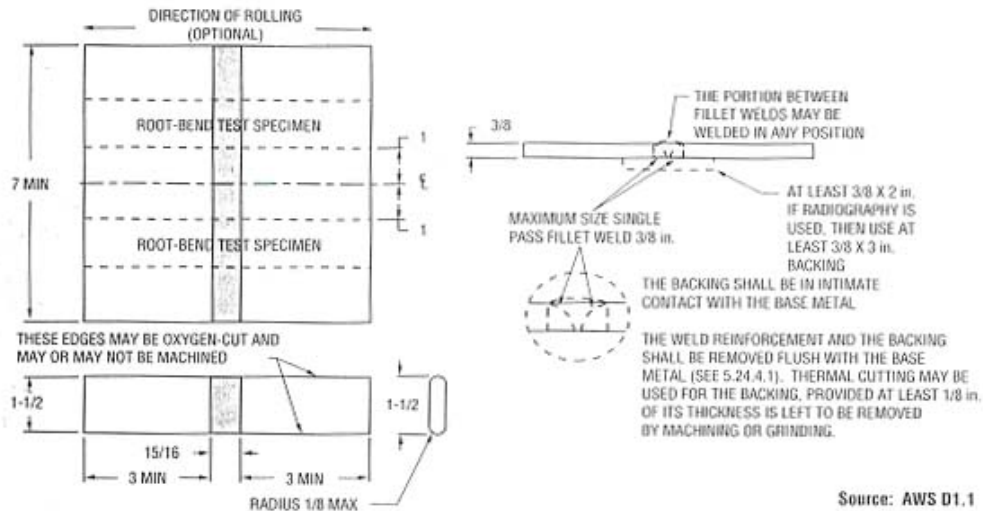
Plancha de ensayo para calificación de soldador AWS para soldaduras de filetes (Opción 2).
